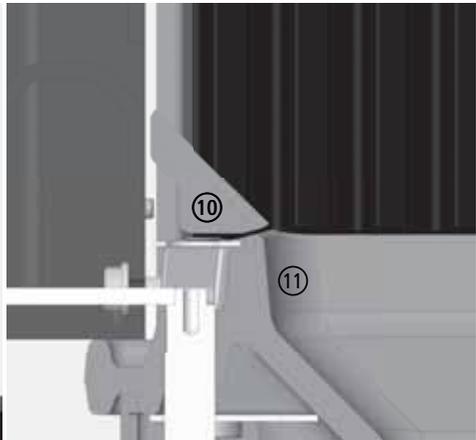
Guss-Anschlussstück (Schnittdarstellung)
